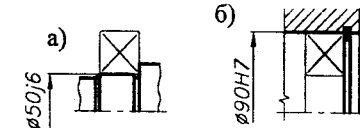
Обозначение посадок мест под подшипники: а) на валу; б) в отверстии корпуса
